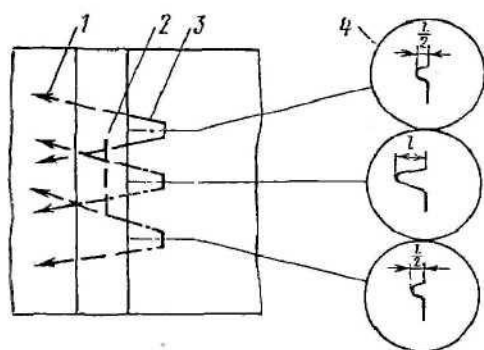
Схема ультразвуковой проверки качества сварного шва:
